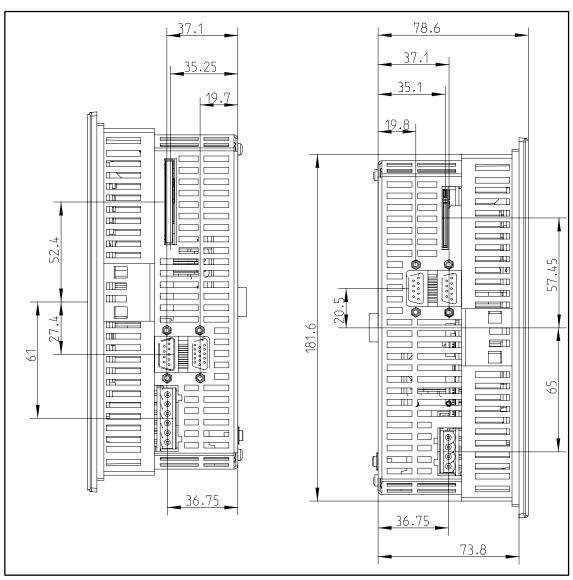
Maßbilder für das C7-635 Touch (Maße in Millimeter)
